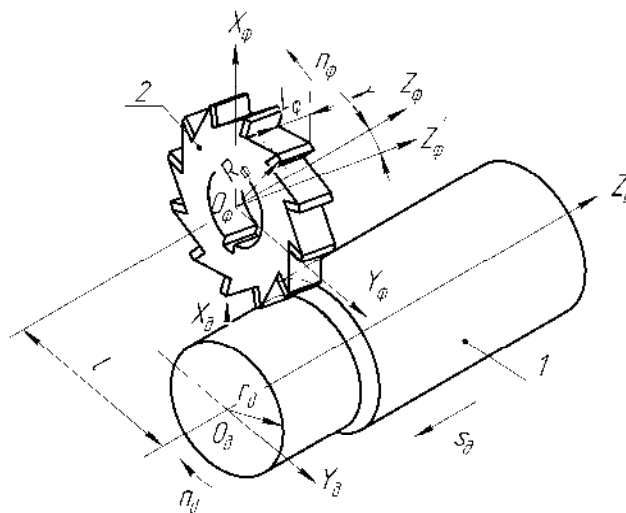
Схема фрезерування циліндричного вала зі схрещеними осями інструмента та деталі
